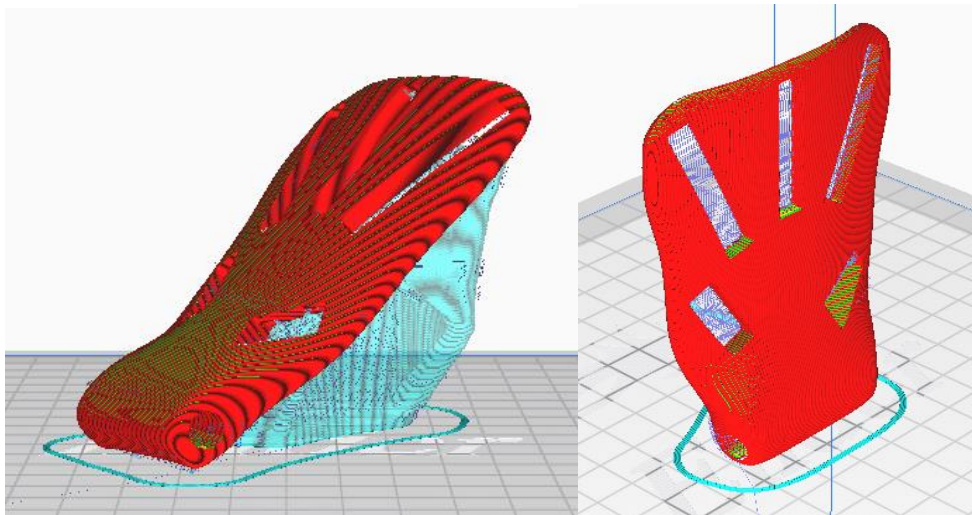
Posicionamiento del elemento a ser impreso con y sin la utilización de soportes (celeste). Fuente: Propia.
